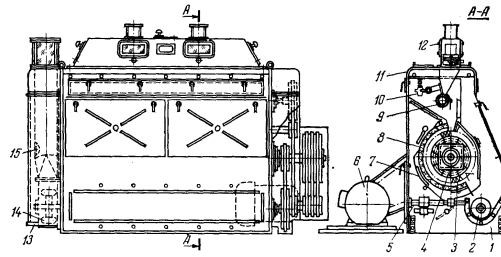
Щіткові машини типу БЩП і БЩМ: 1 – корпус; 2 – шнек; 3 – рухлива щока; 4 – щітковий ротор; 5 – механізм для повороту деки; 6 – електродвигун; 7 – шкала з умовною таріровкою; 8 – щіткова дека; 9 – живильний валик; 10 – механізм для регулювання рівномірності зерна, що надходить; 11 – кришка корпусу; 12 – живильний пристрій; 13 – нижнє вікно корпусу побудника; 14 – побудник броскового типу; 15 – продуктопровід.
